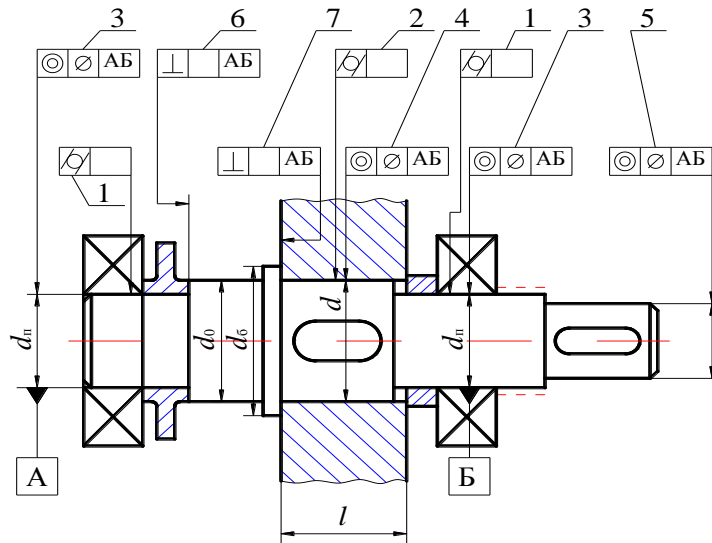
Схема определения допусков формы и расположения поверхностей валов:
